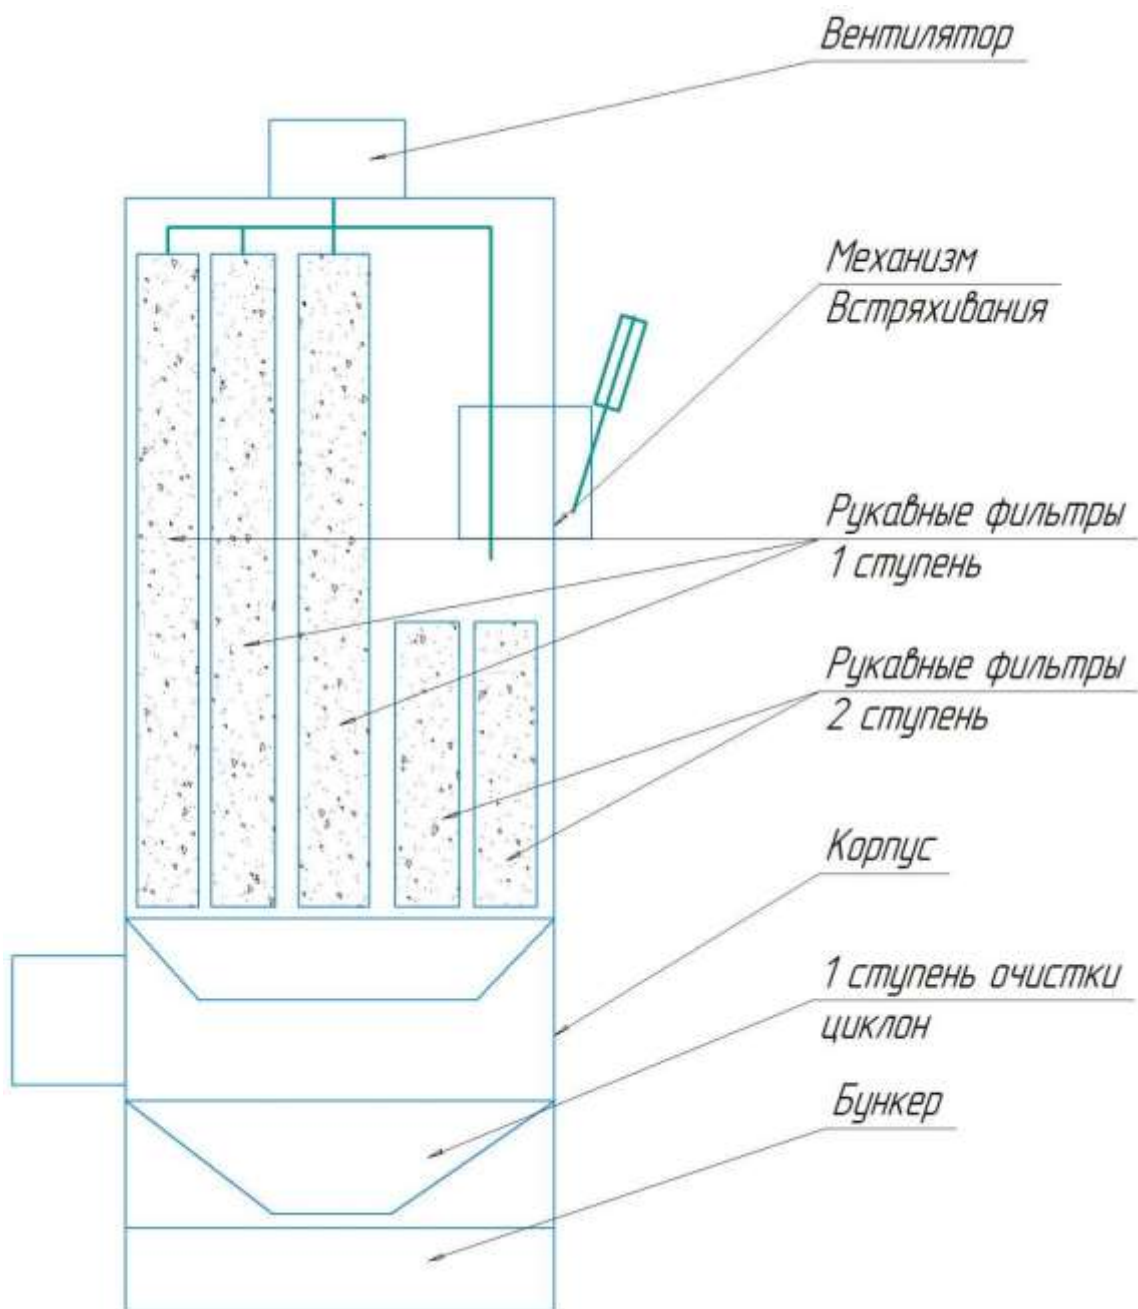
Вентиляционный пылеулавливающий агрегат ЗИЛ-1500
